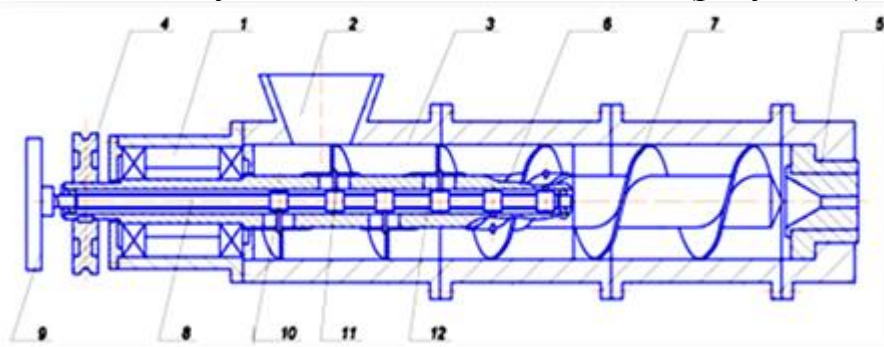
Конструкция одношнекового пресс-экструдера: 1 – подшипниковый узел; 2 – загрузочная воронка; 3 – разъемные корпуса шнековой камеры; 4 – привод; 5 – формующая головка; 6 – шнек; 7 – витки шнека; 8 – резьбовой вал; 9 – приводной механизм; 10 – втулки с установленными пальцами 11; 12 – направляющие
